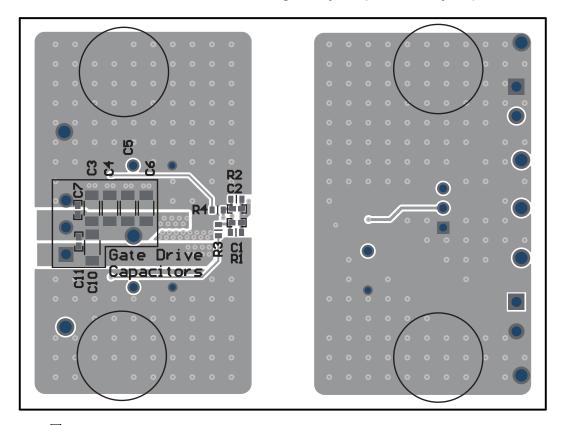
UCC14240EVM-052, PCB Bottom Layer, Assembly (Mirrored View)
